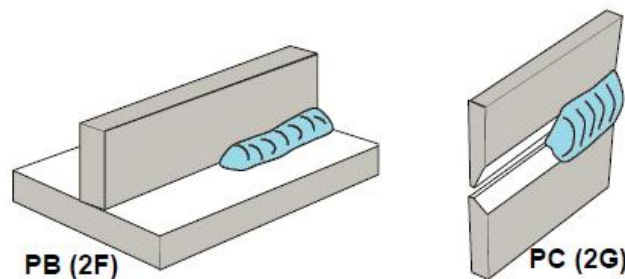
Posições de soldadura horizontal do tipo PB e PC
